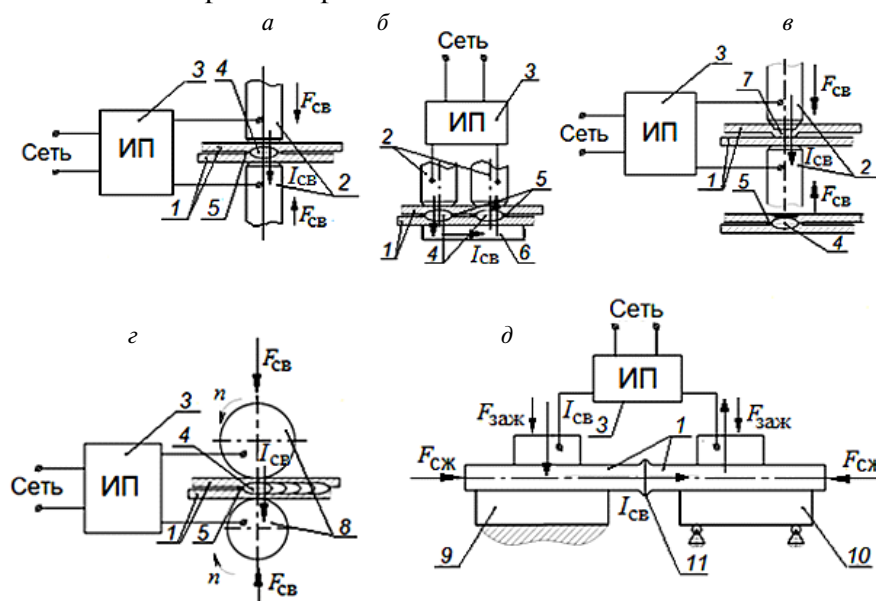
Технологические схемы основных способов контактной сварки
